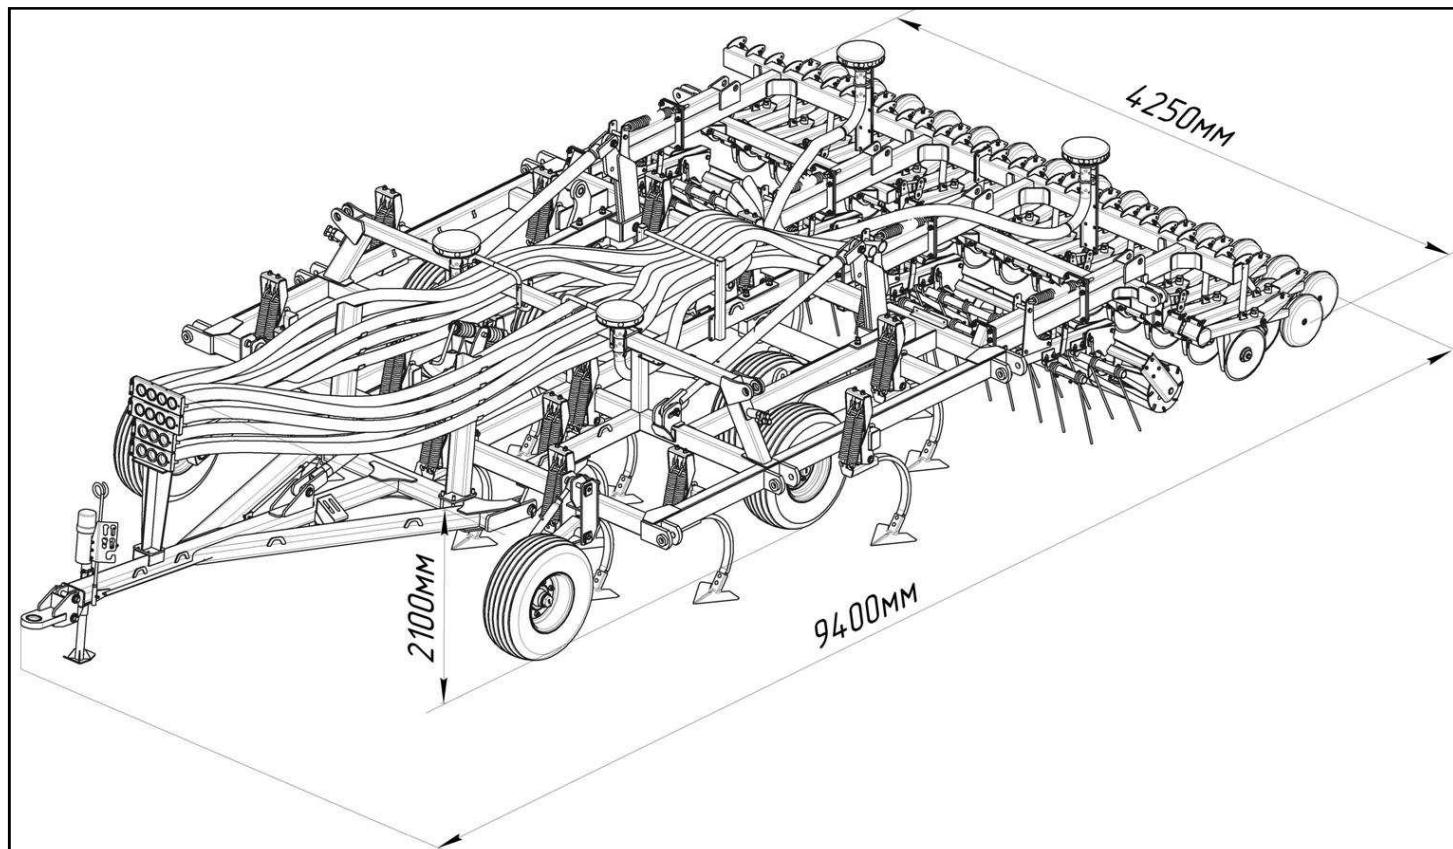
Вид центральной части культиваторной части комплекса при подготовке к транспортированию
